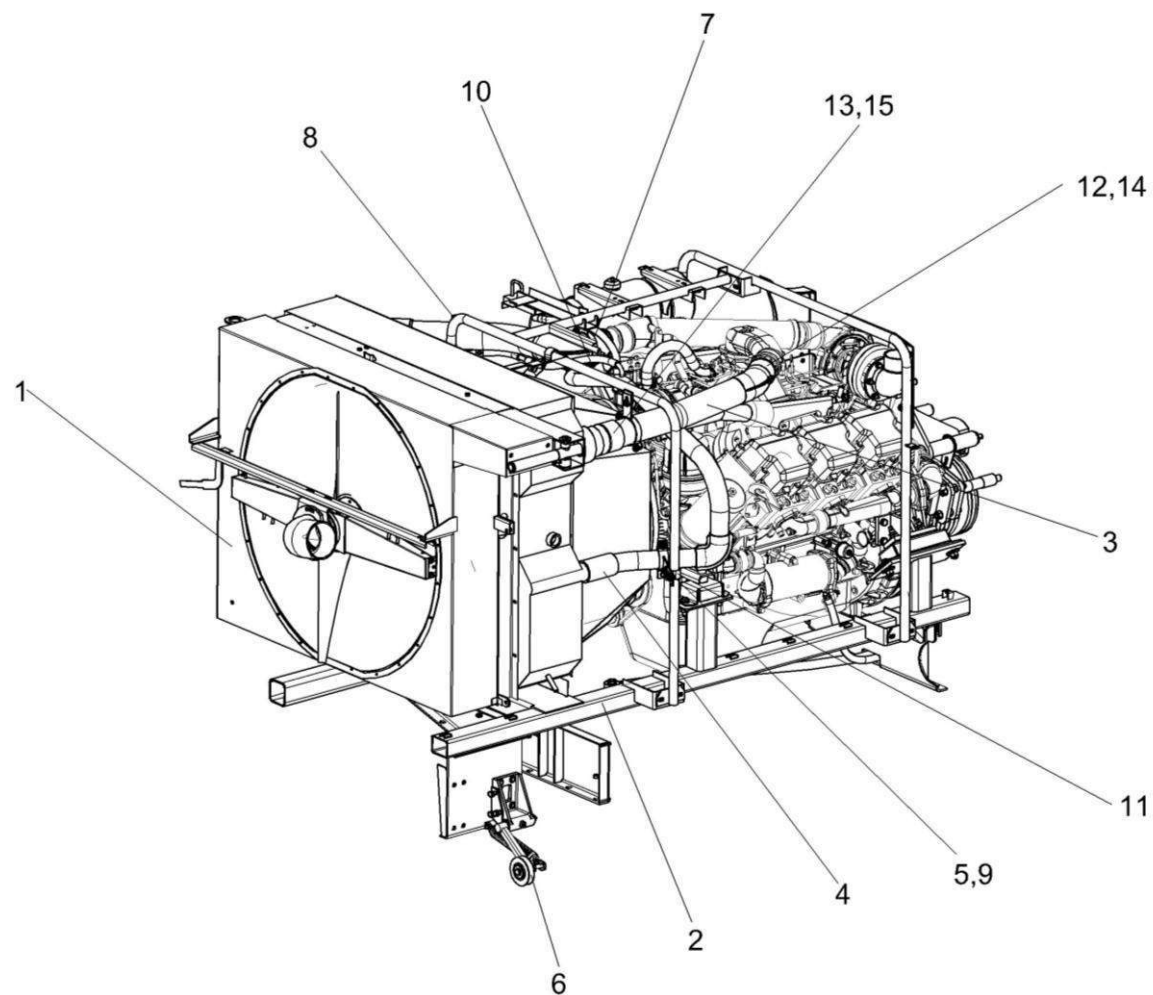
Установка двигателя КЗК-10-2-0106000 (лист 1)
